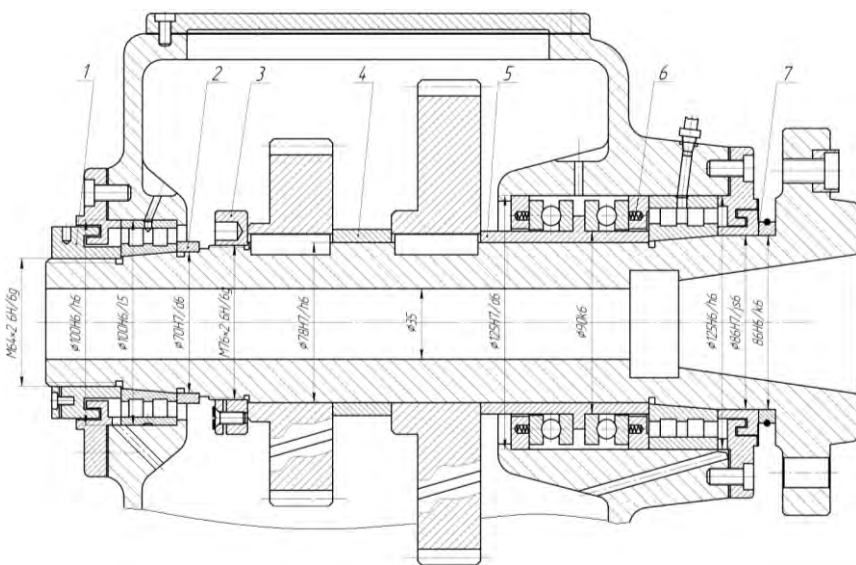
Шпиндельный узел с роликовыми радиальными цилиндрическими подшипниками в опорах и в комплекте с шариковыми упорными – в передней опоре
